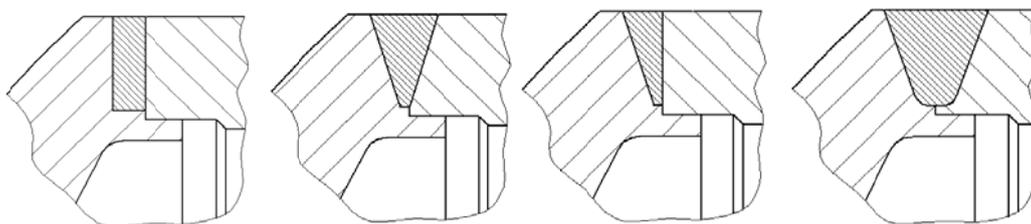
Конструктивное исполнение кромок дна и цилиндра под сварку
